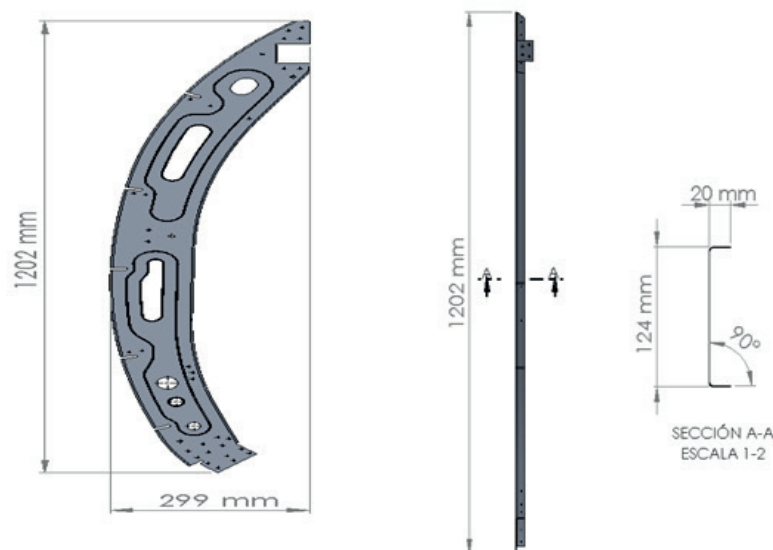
Dimensiones (mm) del lado A de la cuaderna: izquierda, vista frontal; derecha, vista lateral
